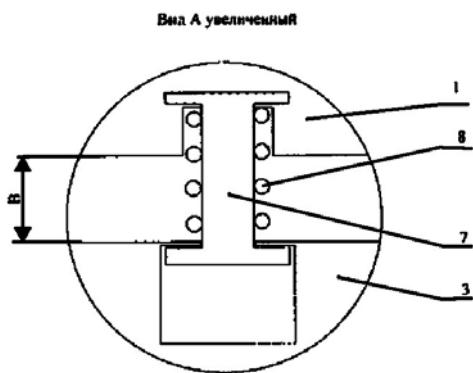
Пружинное соединение рабочей части породоразрушающего инструмента с корпусом
